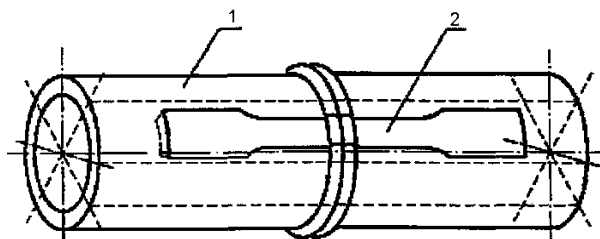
Схема вирізування зразків зі зварного з'єднання для випробування на розтяг, де 1-патрубок зі зварним з'єднанням; 2-розташування зразків [124]
